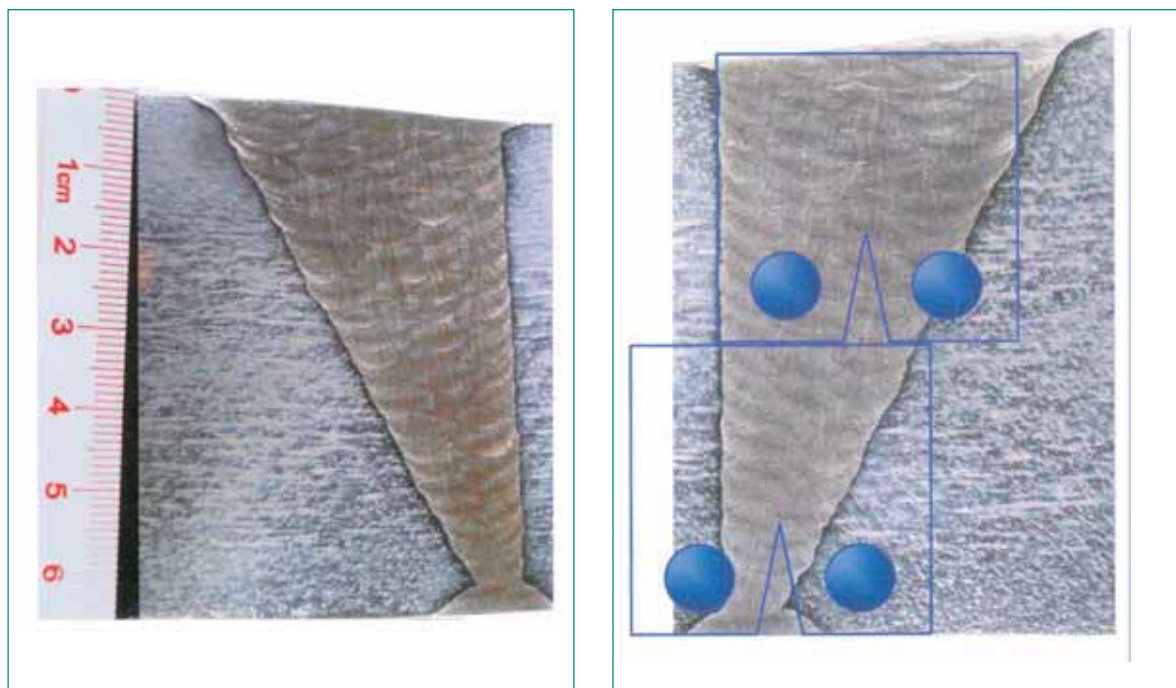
Makroätzung der Inconel-182/Inconel-600-Mischnaht mit Probenlage der 0.5 T-C(T)-Proben zum Studium des Korrosionsrisswachstumsverhaltens im Inconel-182-Schweisgut.
